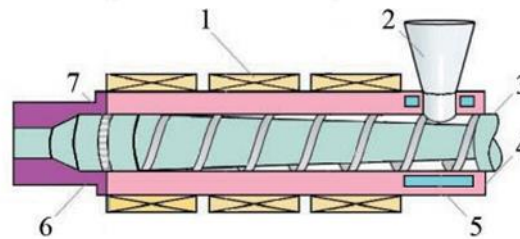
Зерновий прес-екструдер (загальний вигляд): 1 – нагрівач; 2 – бункер; 3 – шнек; 4 – циліндр; 5 – порожнина для циркуляції води; 6 – формуюча голівка; 7 – грати з сітками
